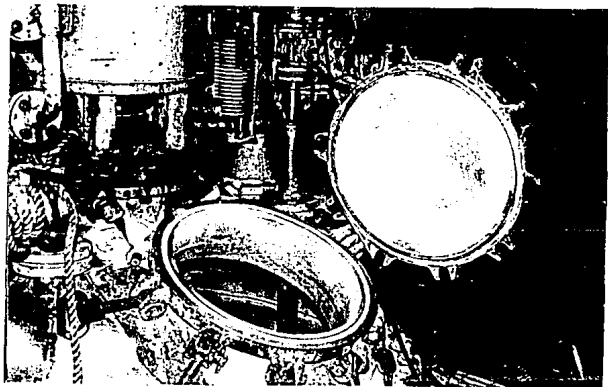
Socavados en la soldadura de reparación.
